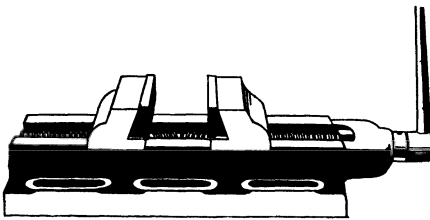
Maschinenschraubstock mit zwei losen Backen.
